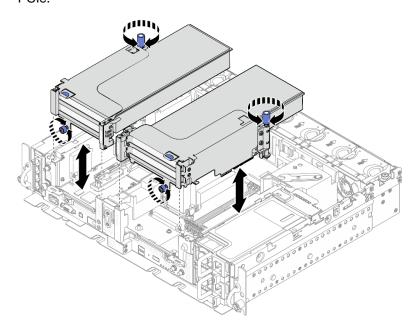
Removendo os conjuntos de placa riser PCle com adaptadores de comprimento integral
